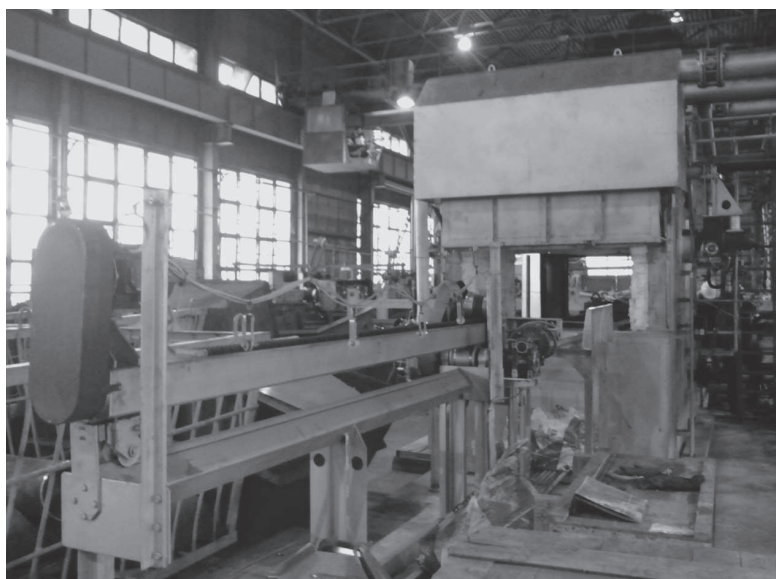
Вид агрегата закалки со стороны загрузочного окна
